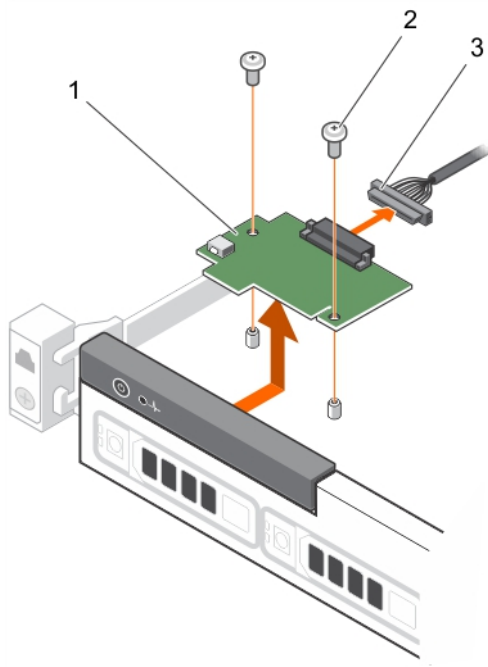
Entfernen des Bedienfeldmoduls – Gehäuse mit vier Festplatten
